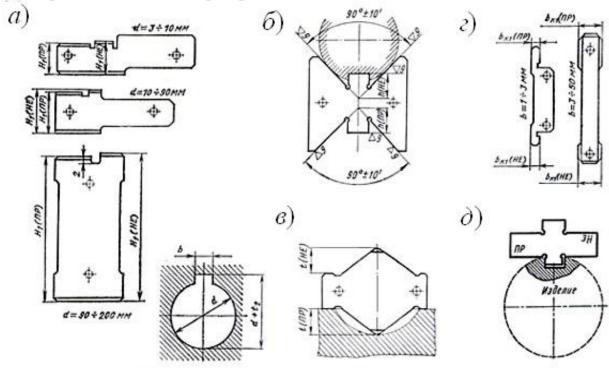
Общий вид калибров для контроля размеров шпоночных пазов: глубиномеры для контроля глубины паза в отверстии (a), на валу (δ) и под сегментные шпонки (b); пазовые калибры для контроля ширины паза (c, δ)
